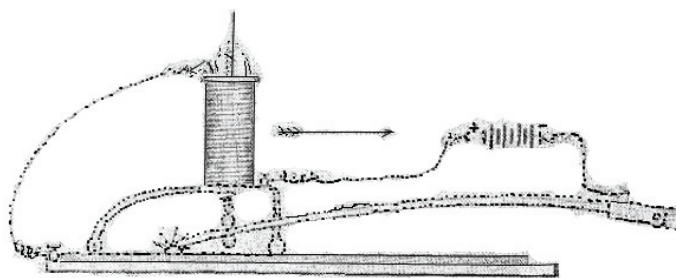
Пристрій для зварювання металевим електродом з автоматичним регулятором дуги (1886)
